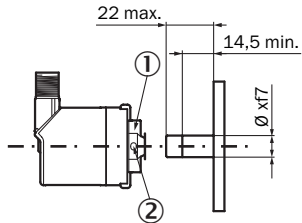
Encoder mit Flansch für Aufsteckhohlwelle (Anbauvorschlag)
